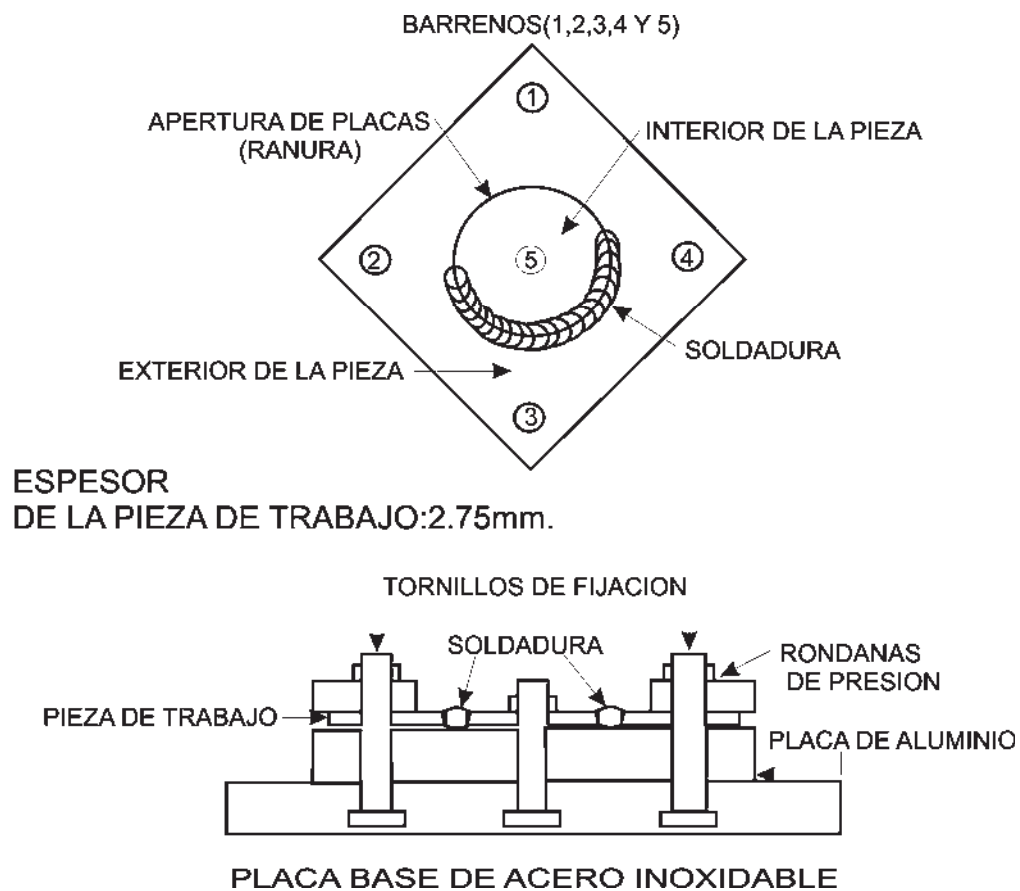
Montaje de probeta estándar del ensayo CPT.
